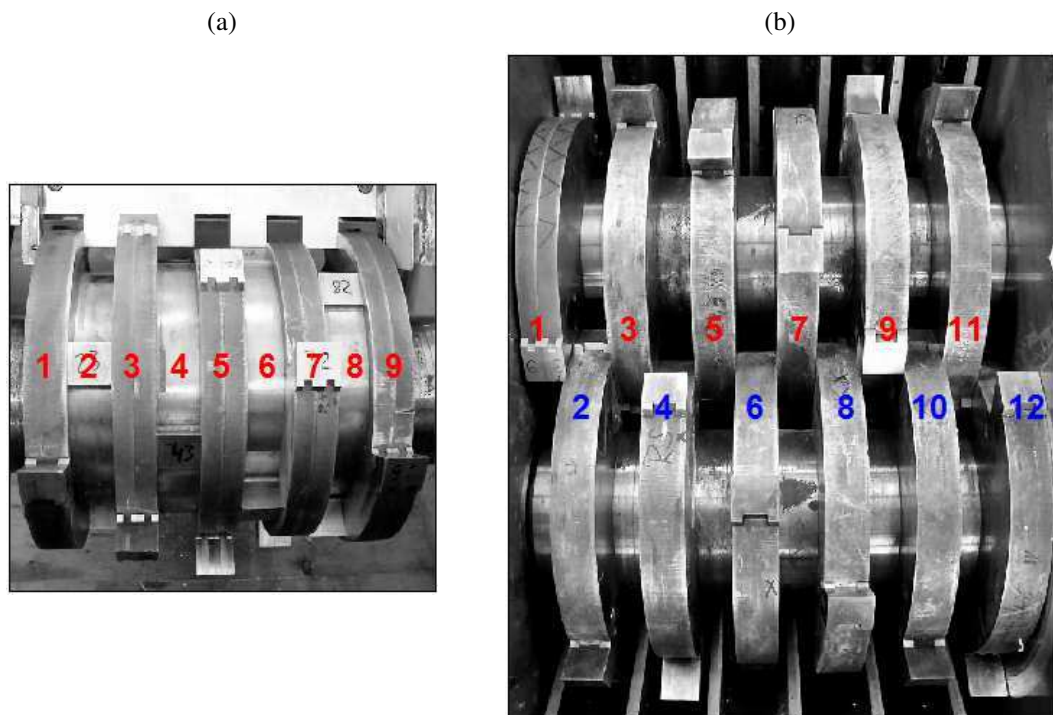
Bezeichnung der Rotorscheiben für die Kennzeichnung der Spalte;
